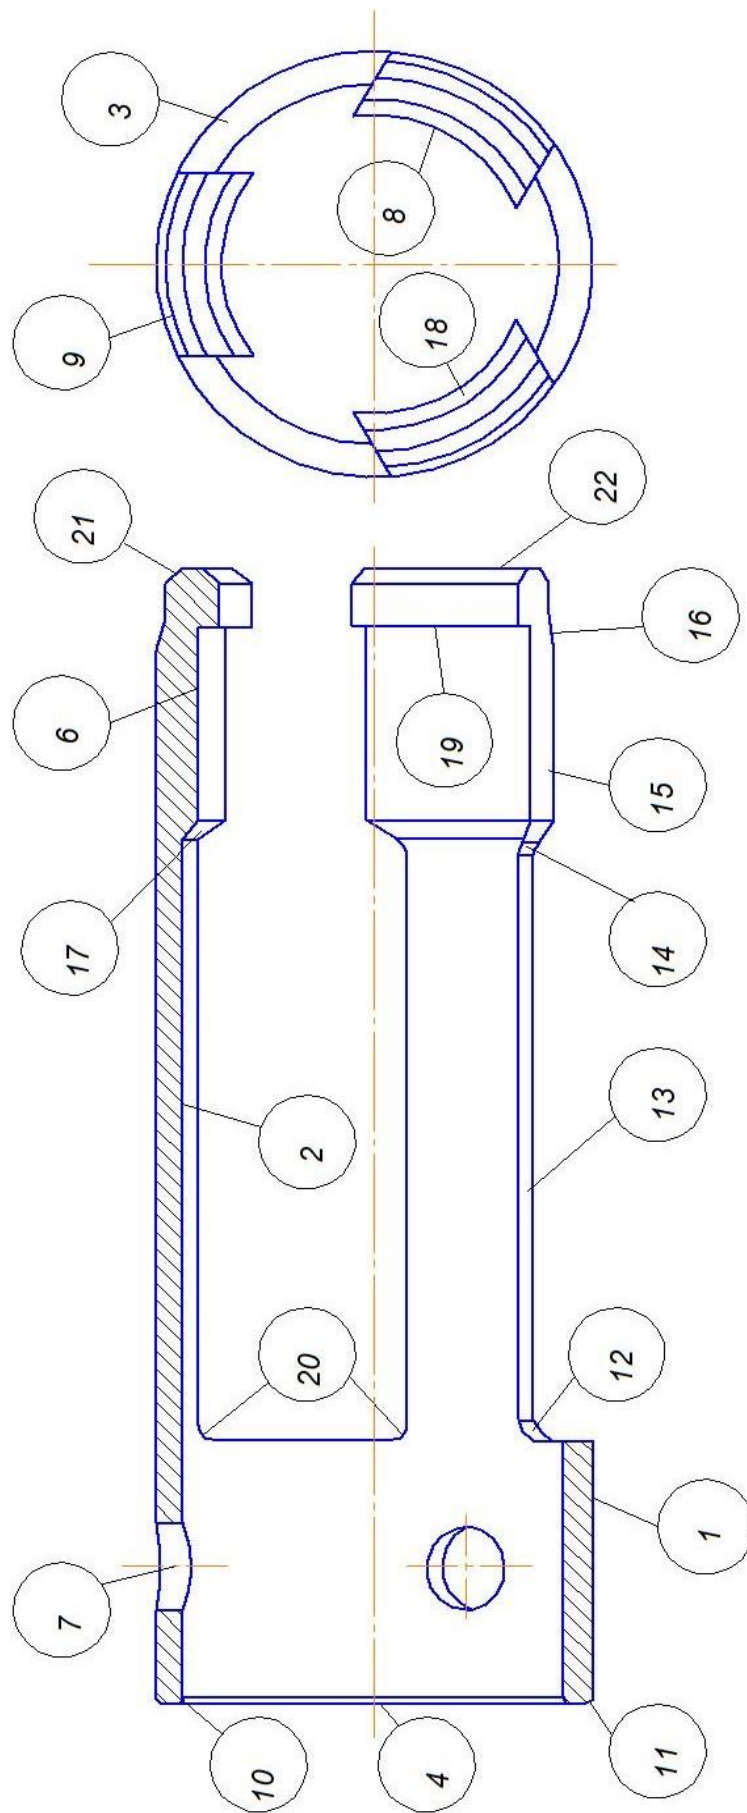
Деталь «Цанга» з номерами поверхонь
